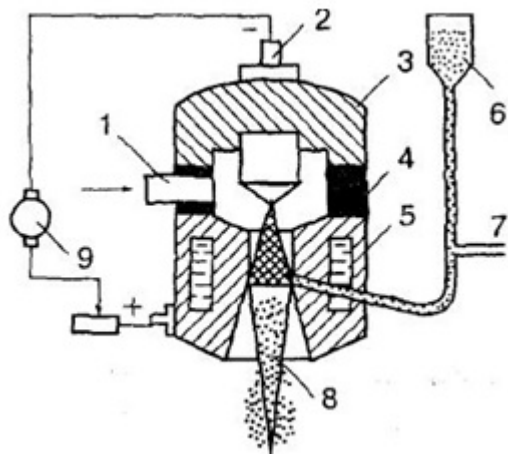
Схема плазменного напыления порошком: 1 — подвод плазмообразующего газа; 2 — катод плазмотрона; 3 — корпус; 4 — изолятор; 5 — анод; 6 — порошковый питатель; 7 — подвод газа, транспортирующего порошок; 8 — плазменная дуга; 9 — блок питания. [1]
